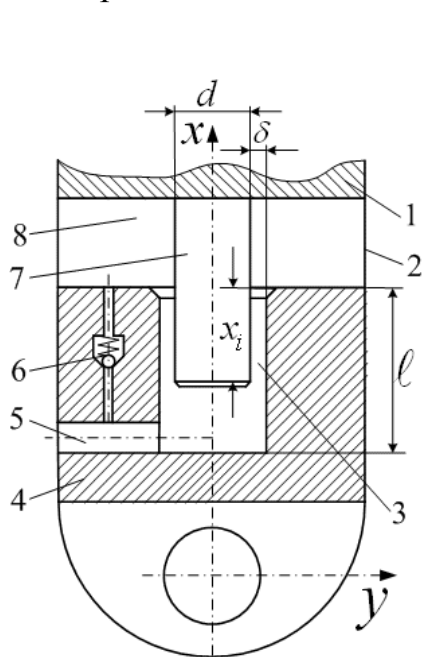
Конструкція демпферного пристрою при гальмуванні об'ємом рідини з поршневої порожнини гідроциліндра
